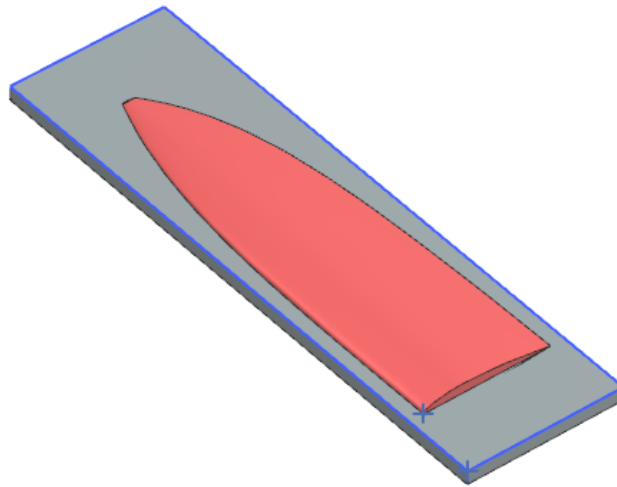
Diseño del molde en SIEMENS NX.
